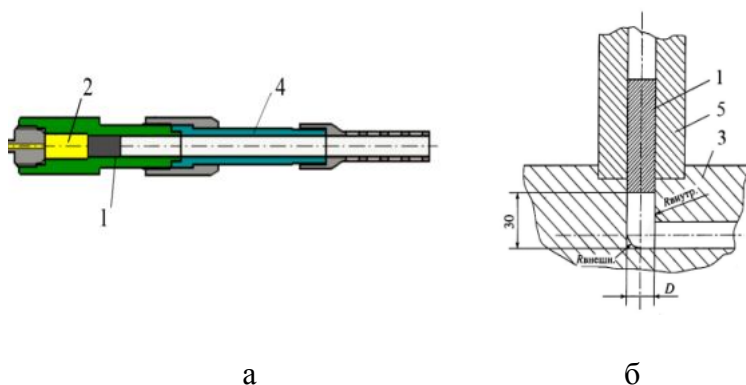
Схема установки ДКУП: а - устройство для разгона образцов, б - матрица; 1 - образец; 2 - пороховой заряд; 3 - матрица; 4 - ствол; 5 - направляющая втулка.
